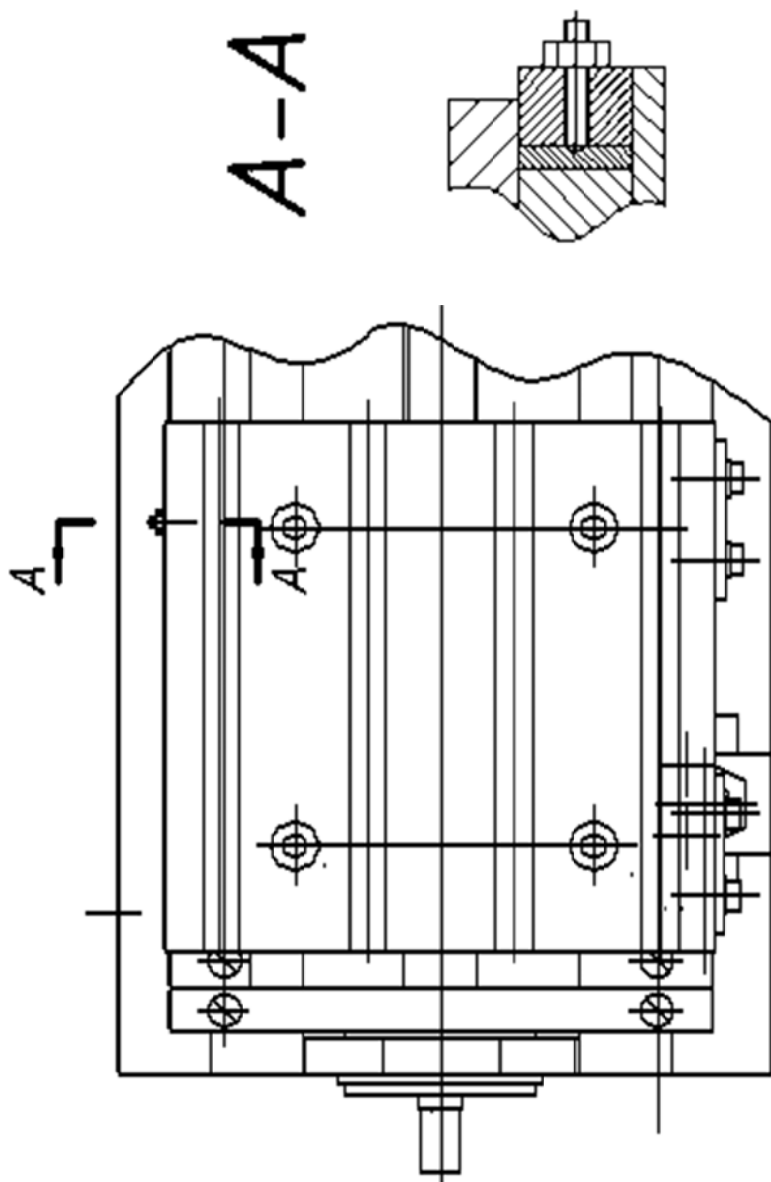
Подвижный стол с направляющими скольжения – вид сверху
